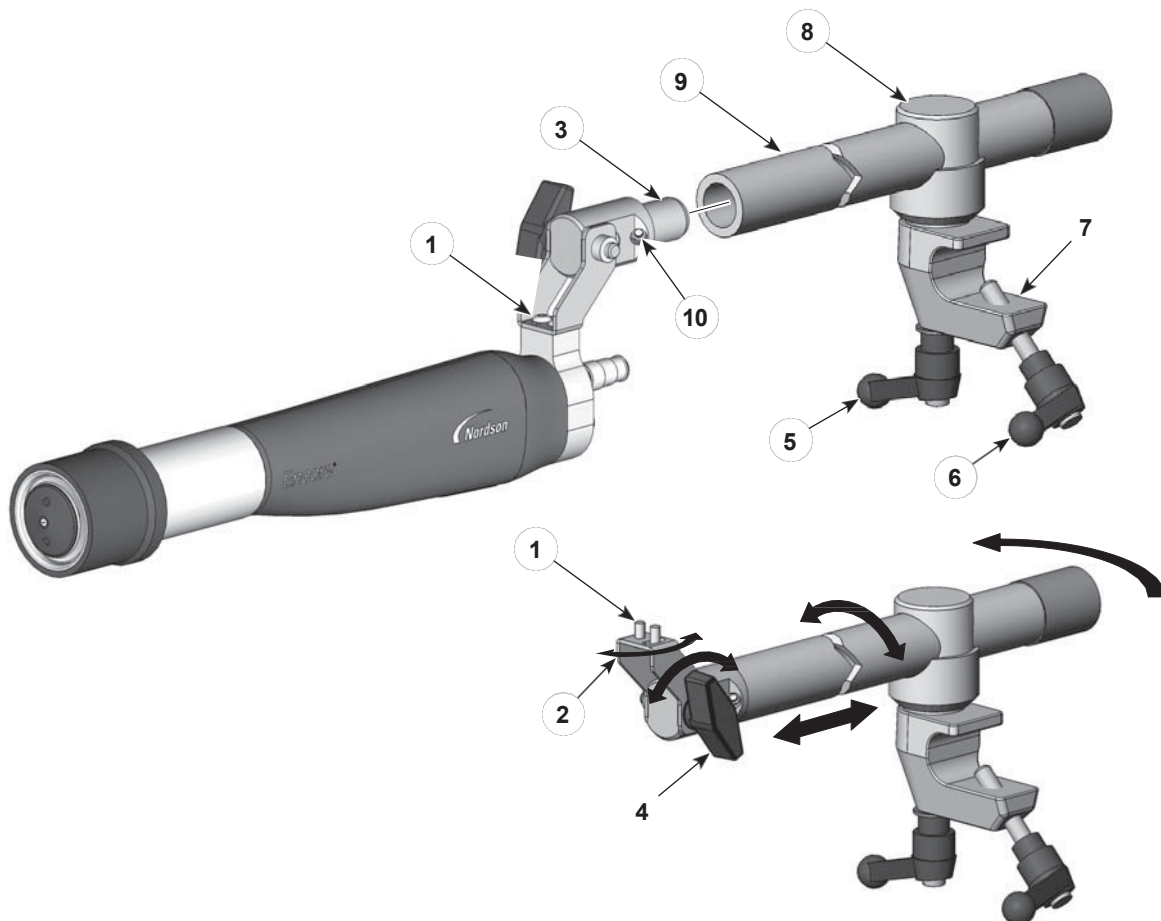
Standard Gelenkstangenmontage der Pistole
